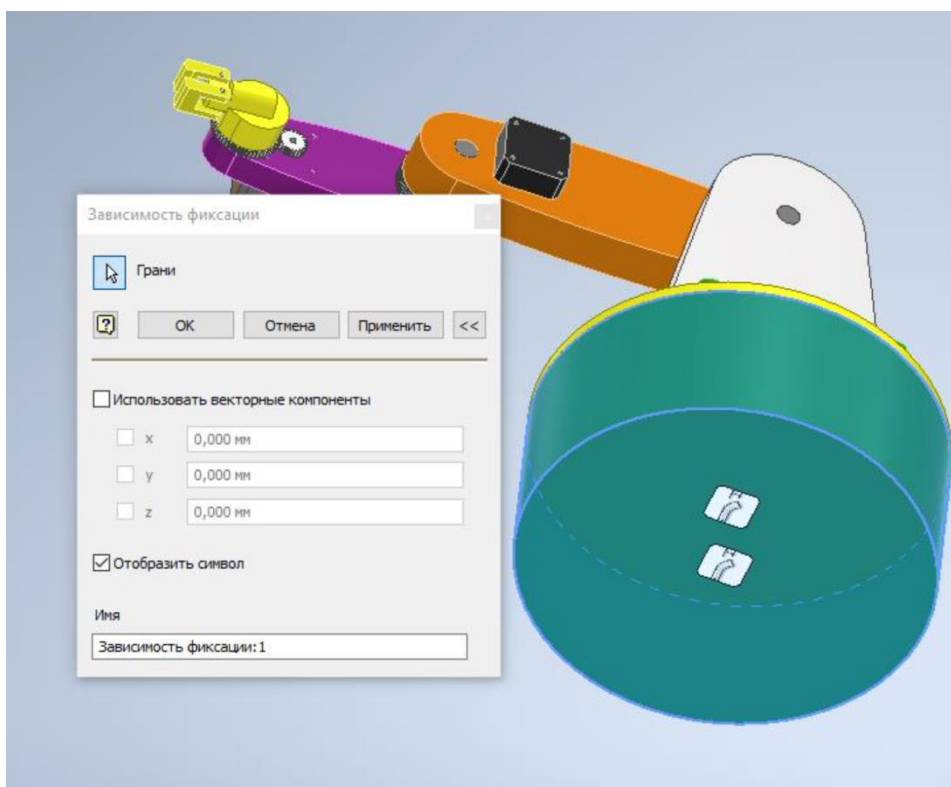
Фіксація корпусу поворотної платформи
